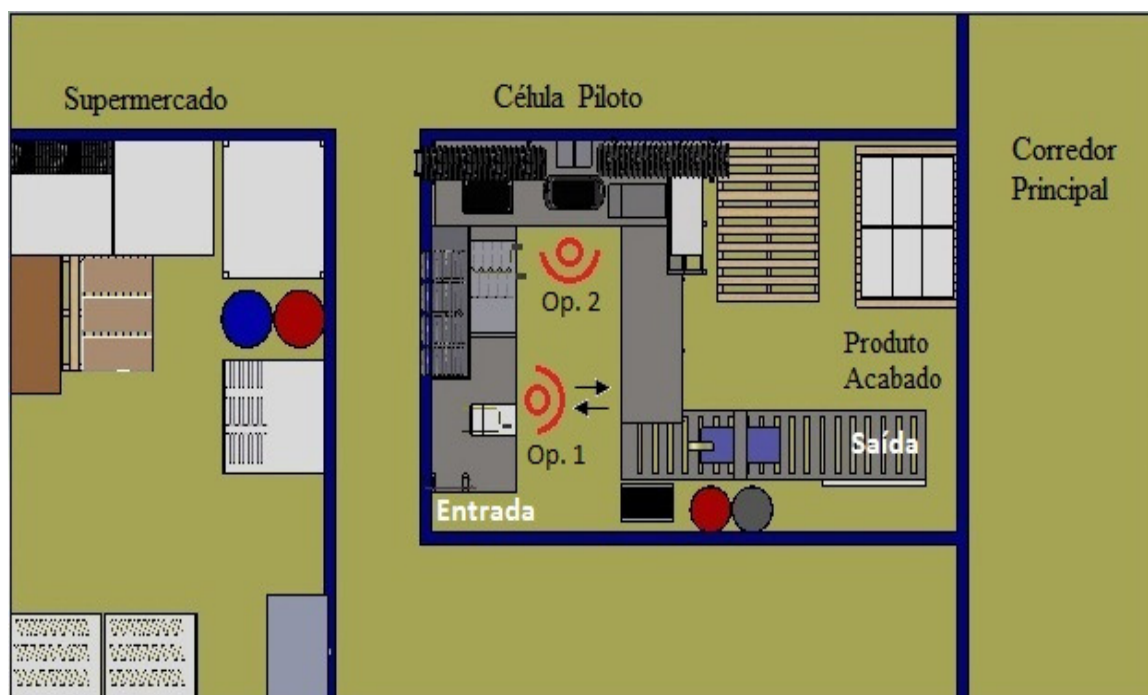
Planta baixa da célula e do supermercado. Fonte: dados da empresa (2010).
